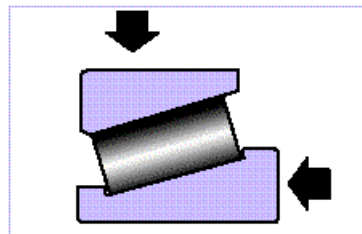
Combinación de carga radial y axial en un rodamiento cónico.
